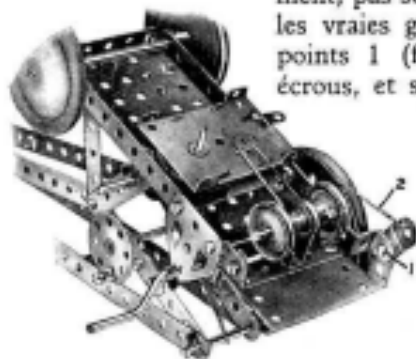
Le châssis de la grue mobile de la fig. 5, vu par en dessous, avec le Moteur « Magic ».
